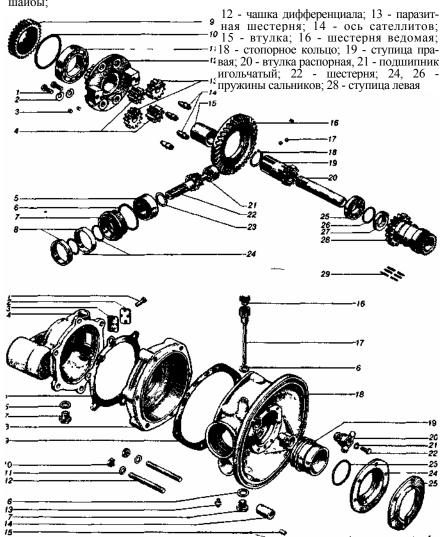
Картеры и крышки дифференциала мотоциклов "Днепр-11/16": 1,15 - винты; 2 - крышка; 3 - прокладка; 4 - крышка дифференциала; 5 - прокладка; 6 - прокладка; 7 - пробка; 8 - картер дифференциала; 9 - прокладка; 10 - гайка; 11,21 - шайбы, 12 - шпилька; 13 - масленка; 14 - втулка кулака; 16 - пробка сапуна; 17 - щуп; 18 - картер; 19 - втулка; 20 - кронштейн; 22 - болт; 23 - пружина сальника; 24 - воротник сальника; 25 - крышка сальника
